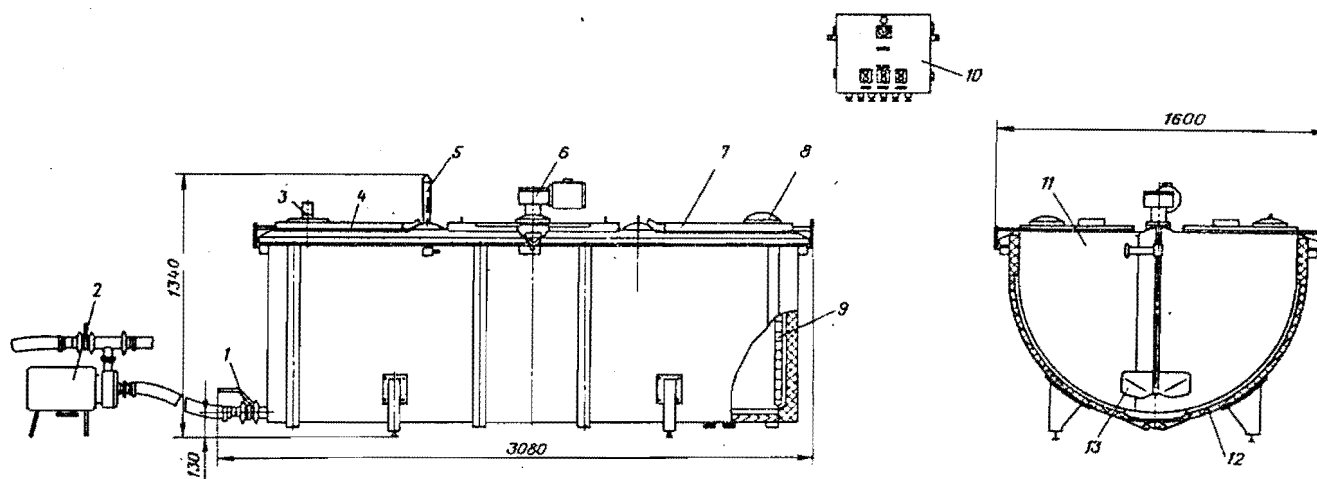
Общий вид резервуара молочного марки РПО-1,6:
